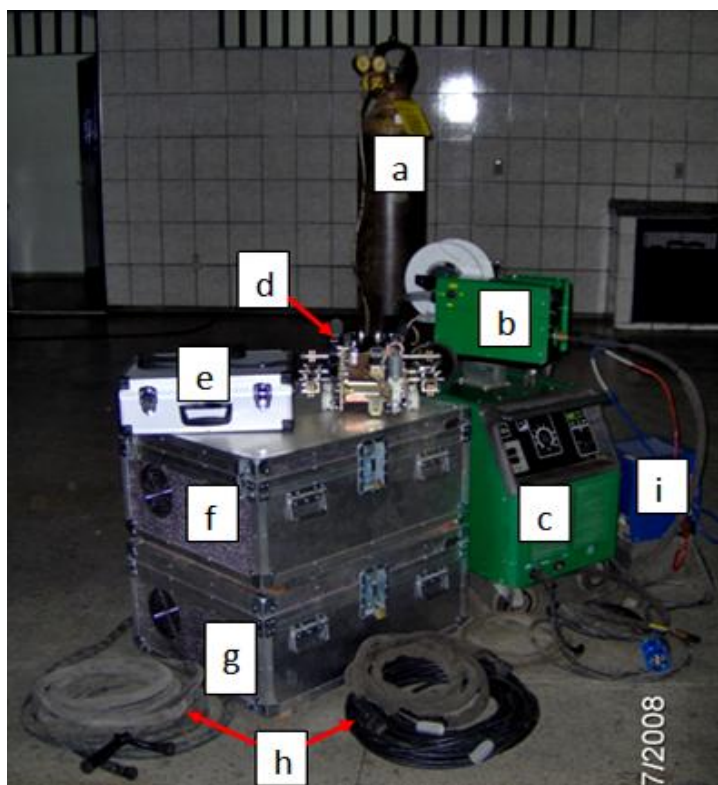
Sistema Orbital para soldagem de tubulação.
